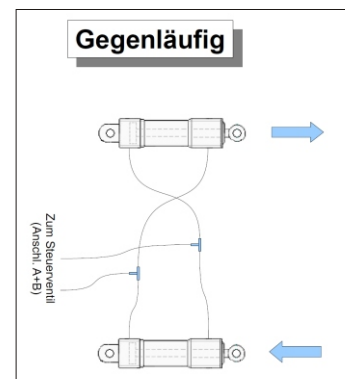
zeigt symbolisch wie der Schwenkzylinder verschlaucht wird.
